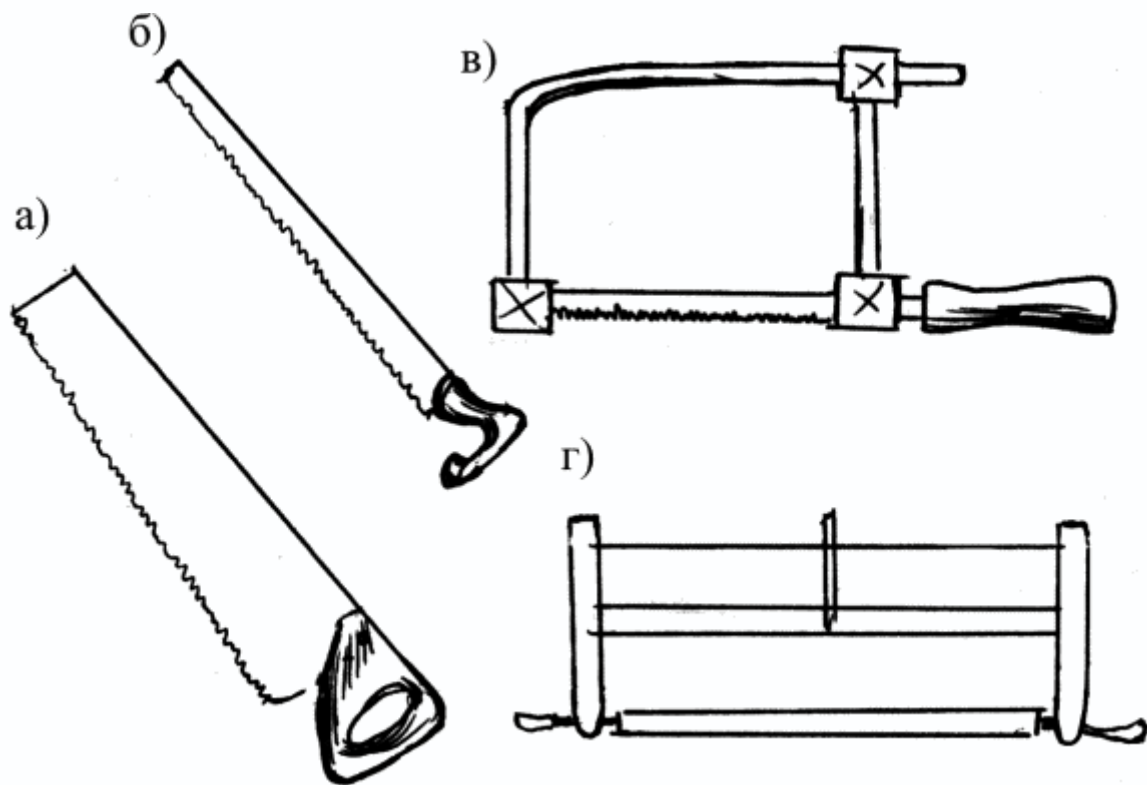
Инструмент для пиления: а – поперечная ножовка (широкая); б – узкая ножовка; в – ножовка с обушком; г – лучковая пила
